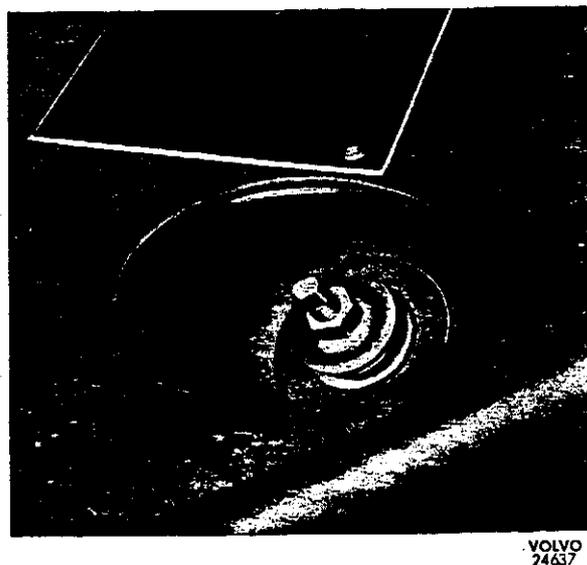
Obere Halterung des hinteren Stoßdämpfers, 1800
